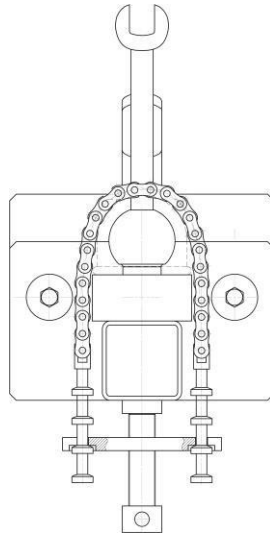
Внешний вид нагрузателя сцепного устройства.
